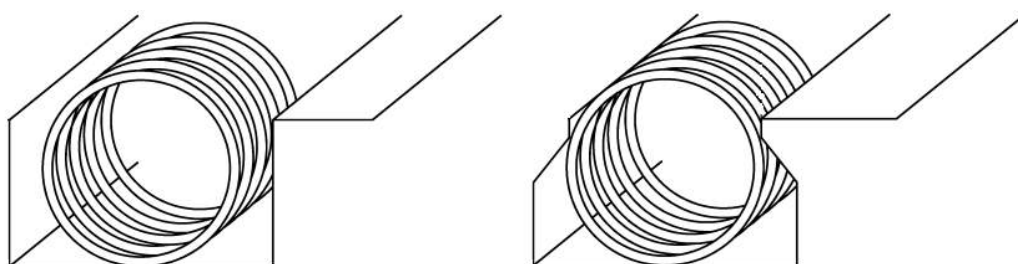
Установка спиральных прокладок в канавки корпуса
